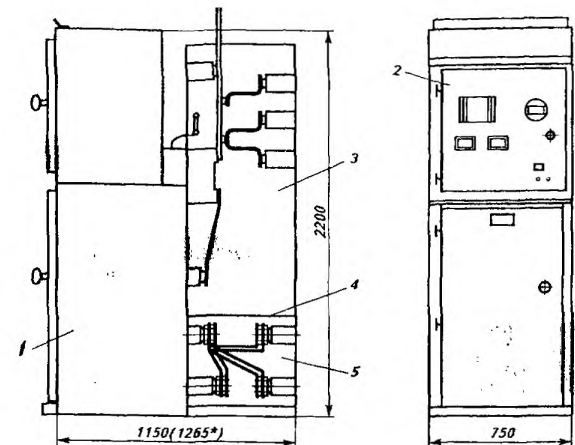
Шкафы КРУ серий К-104 и К-104МС1 с выключателями и шинными вводами сверху
